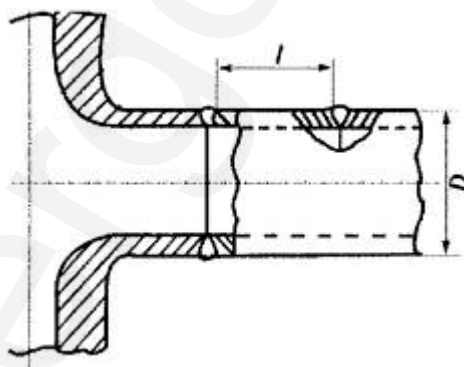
Расположение сварных соединений трубопровода с патрубком
